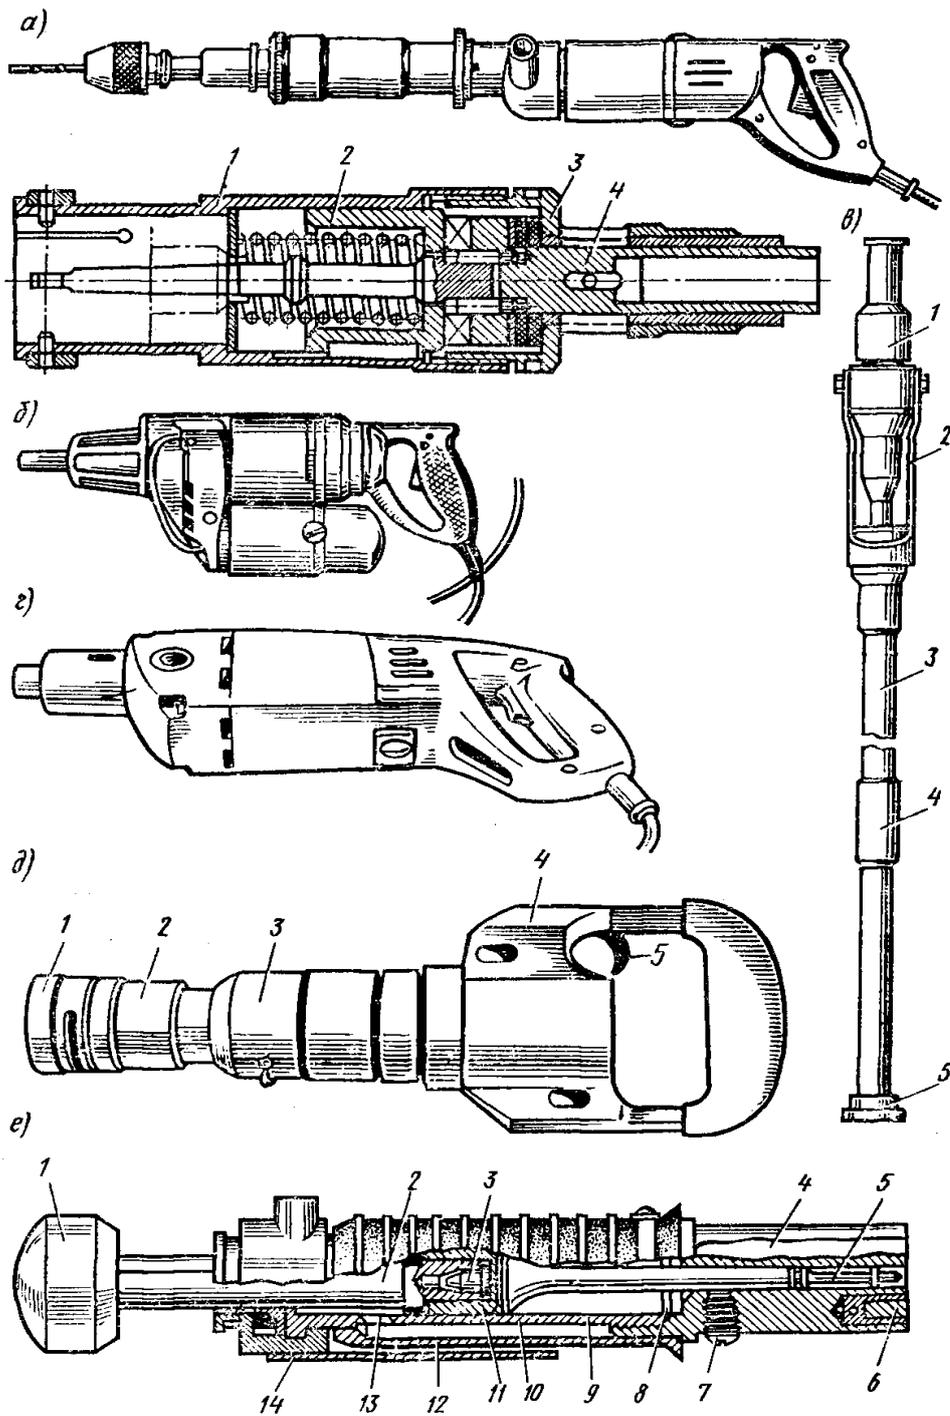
Инструмент для подготовки креплений электропроводок:
